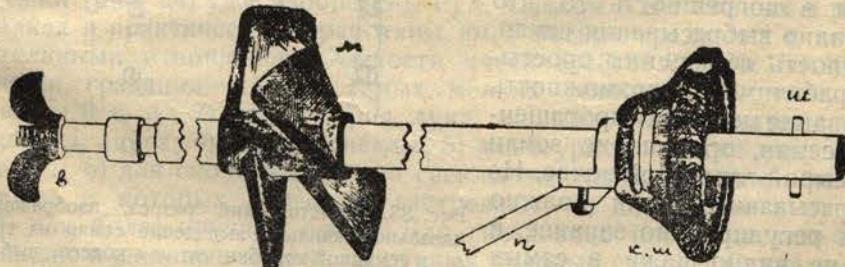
Подвижная ось, проходящая с мотыльком через посевную коробку: ш—шипы для захвата конической шестерни к.ш; п—прут от шестерни к передней раме, м—мотылок, в—винт для укрепления лекал.
